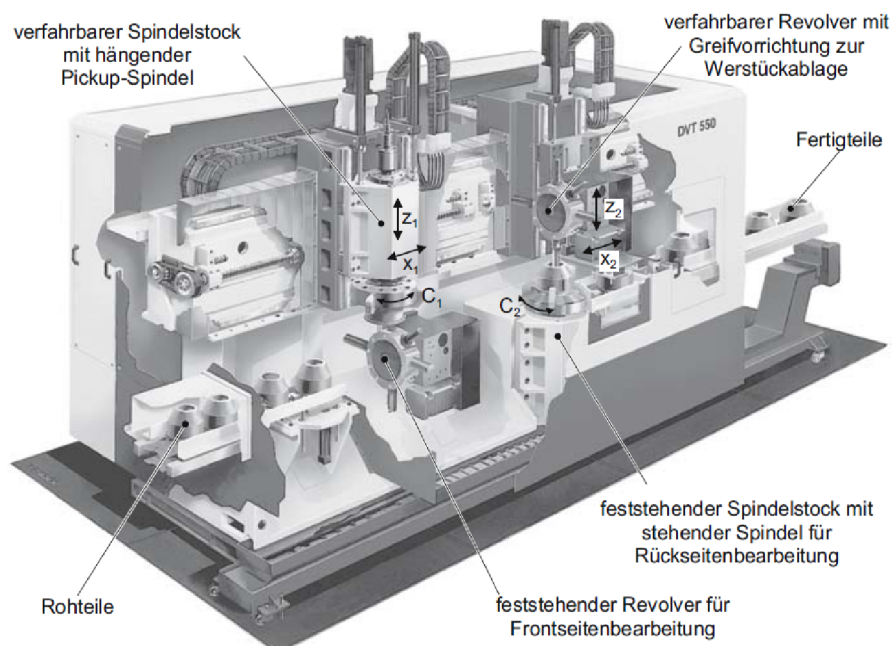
Zwischenspindel-Senkrechtdrehmaschine [8].
